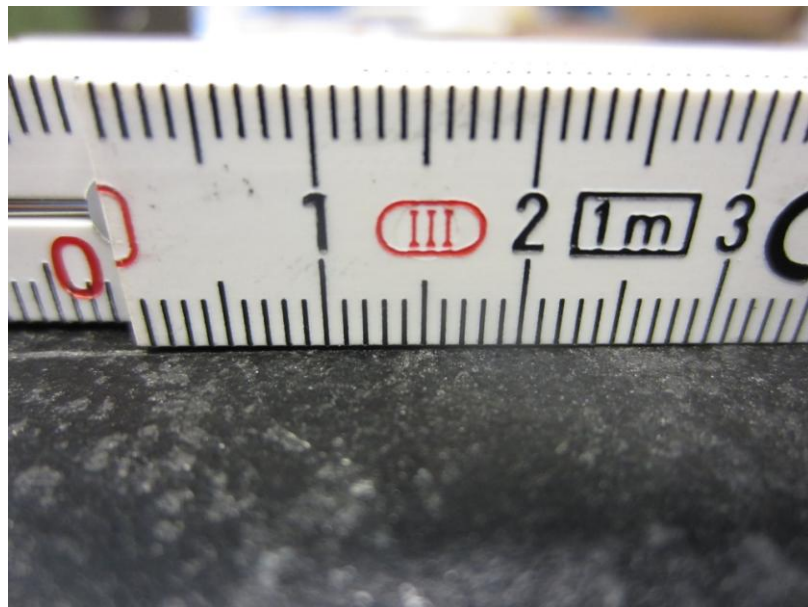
Gusseisenoberfläche einer handelsüblichen Ablauftasse
